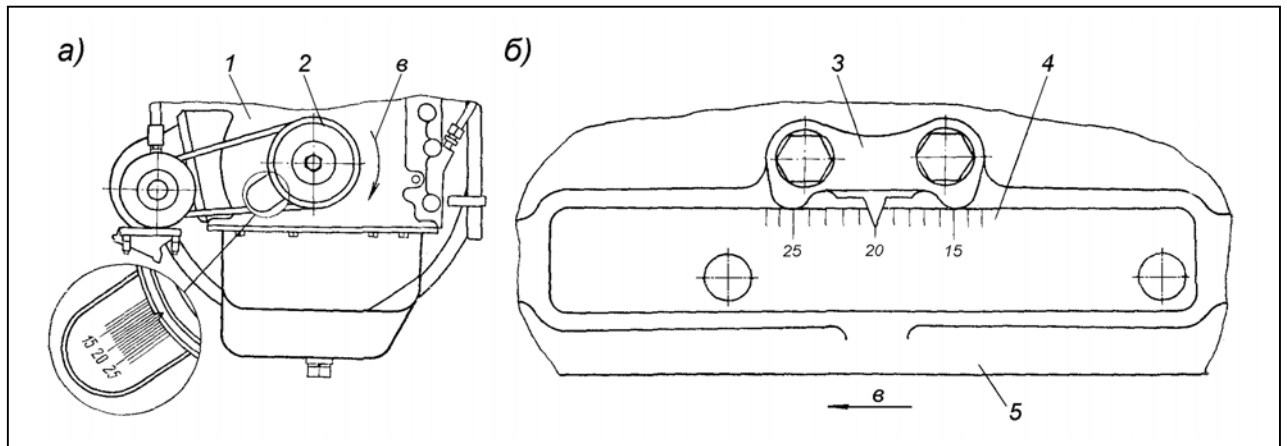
К установке положения коленчатого вала при соединении муфты привода ТНВД двигателей ЯМЗ-236,-238 (для модиф., снятых с производства); положение рисков и меток: а) – на шкиве коленчатого вала и крышке шестерен распределения; б) – на маховике; в) – направление вращения коленчатого вала; 1 – крышка шестерен распределения; 2 – шкив коленчатого вала; 3 – указатель; 4 – маховик; 5 – картер маховика.
